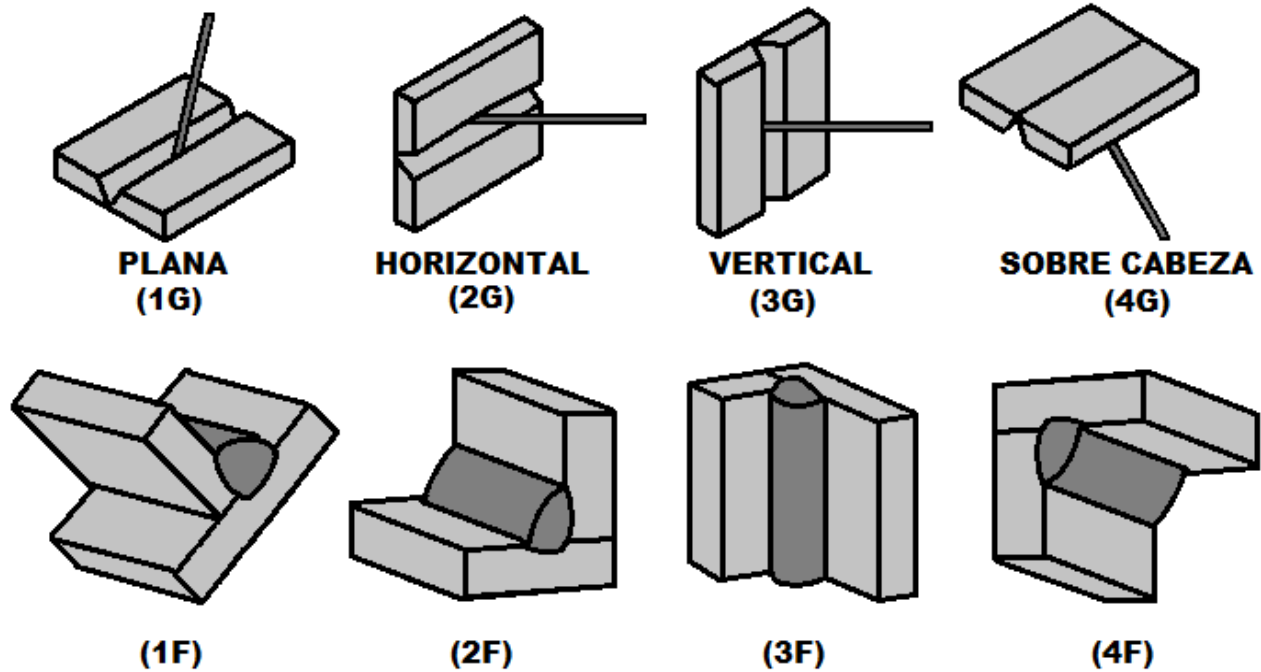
Tipos de posiciones de soldadura (2, 3, 18, 30)
